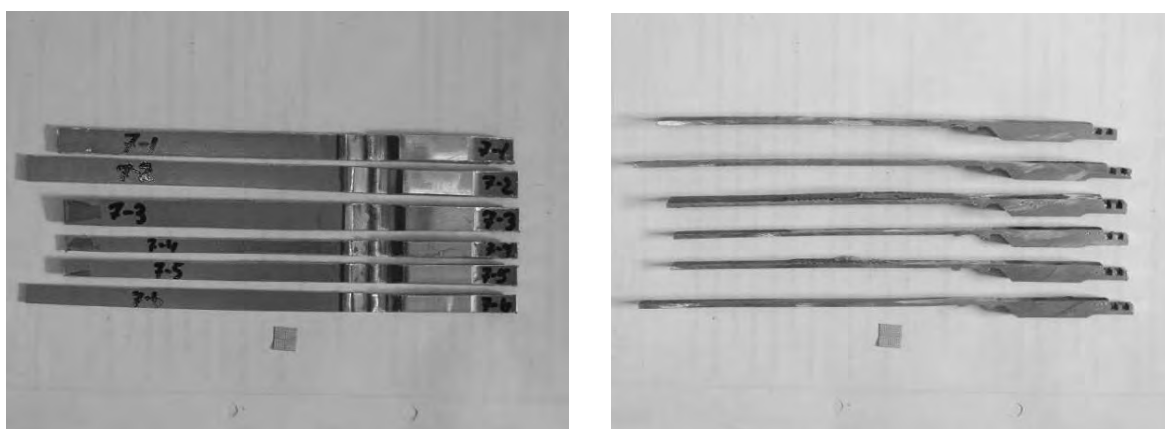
Внешний вид образцов для проведения механических испытаний со сварным соединением, полученным с использованием предлагаемой технологии ремонта
